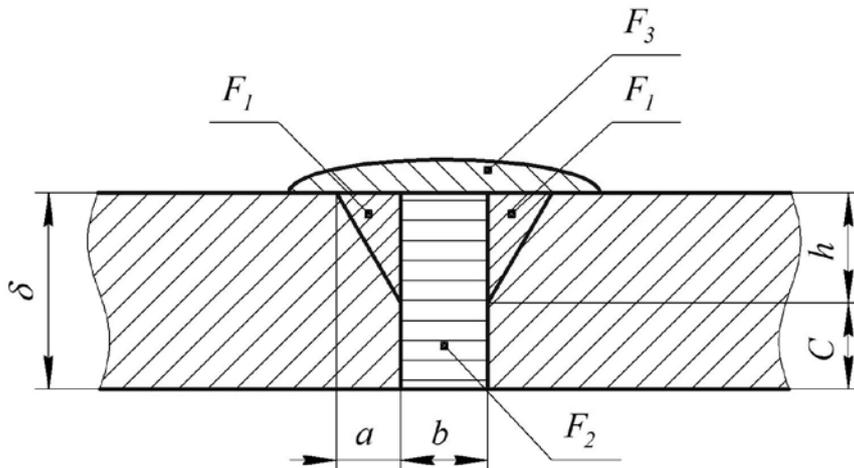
Чертеж стыкового шва сварного соединения ( $b = 2...4$ ,  $C = 2...4$ )
